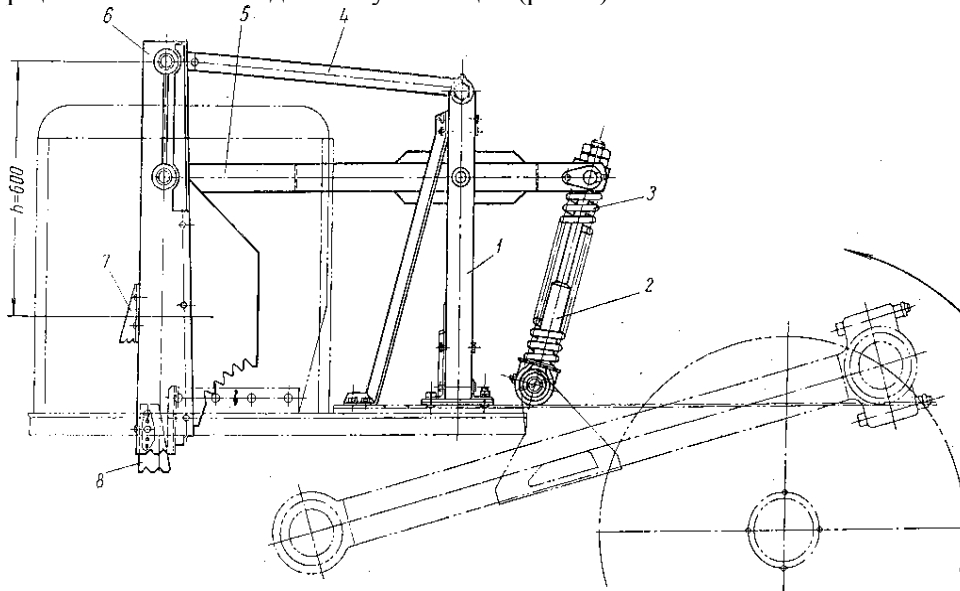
Набиватель: 1 – стойка, 2 – шатун, 3 – пружина, 4 – рычаг, 5 – коромысло, 6 – уплотнитель, 7 – козырек, 8 – надставка уплотнителя
